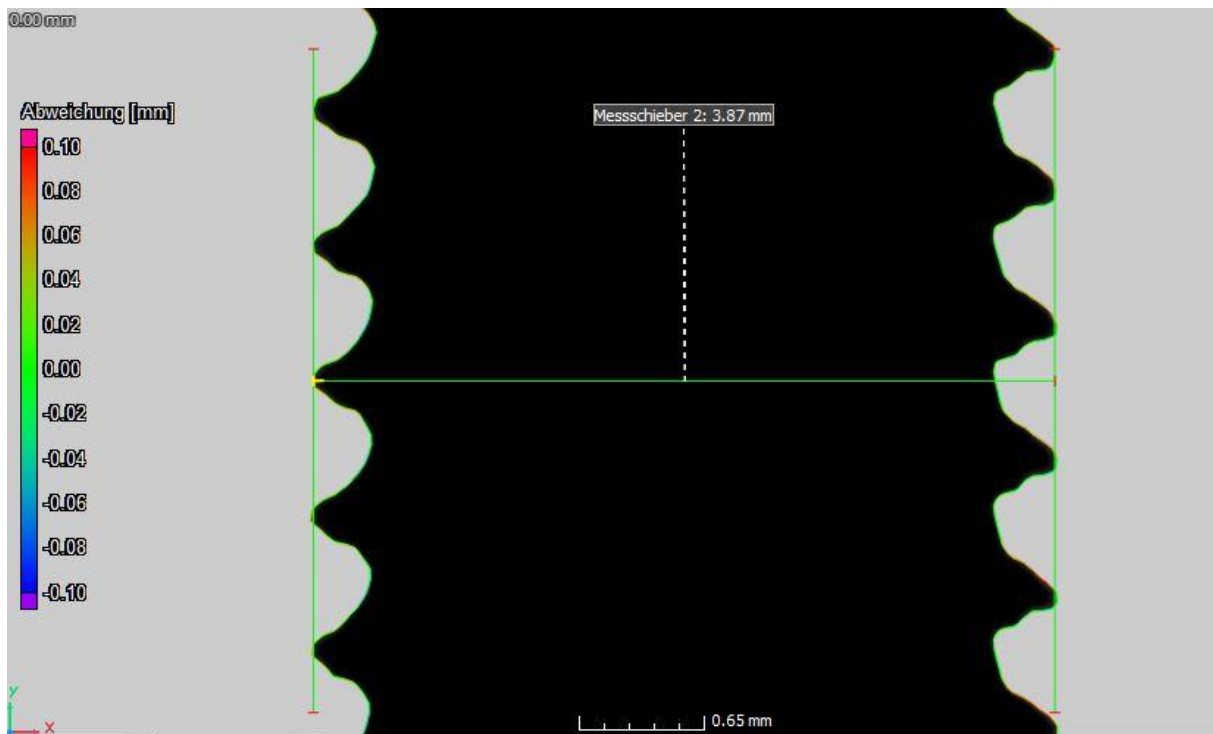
Probe "1-Z" M4 Außendurchmesser
